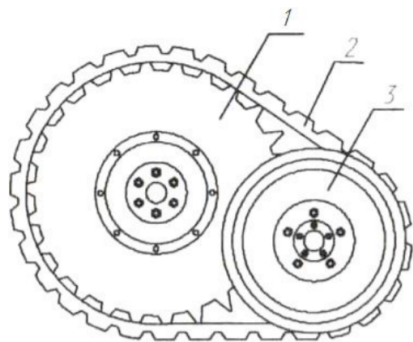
Полугусеничный движитель с направляющими дисками
